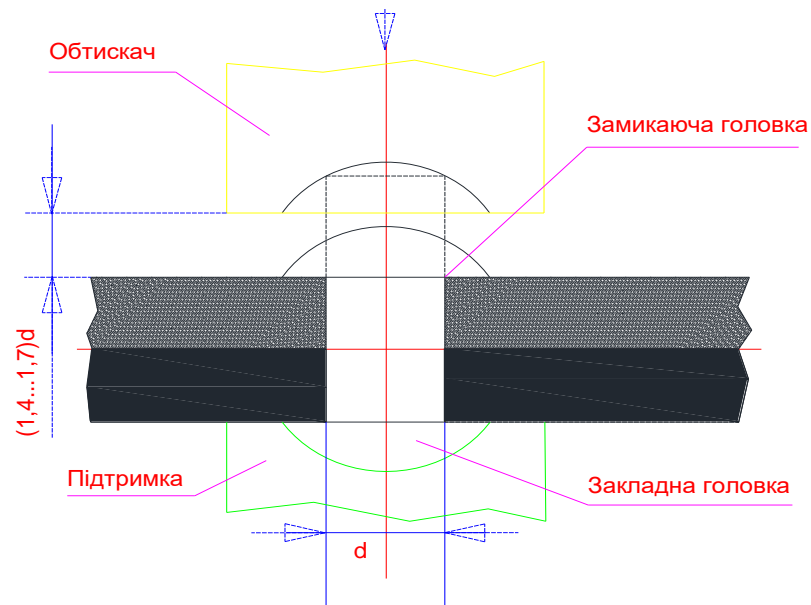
Загальний механізм клепкового з'єднання
